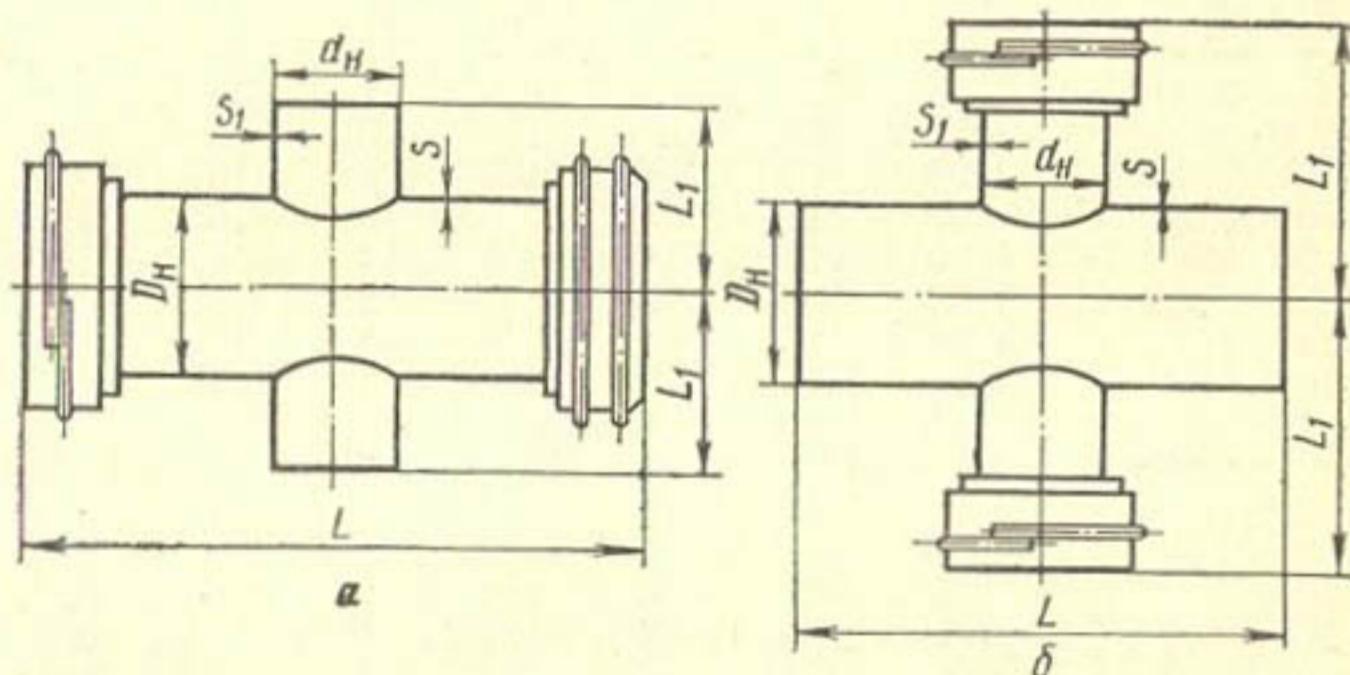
Кресты для соединения металлических и железобетонных труб.
